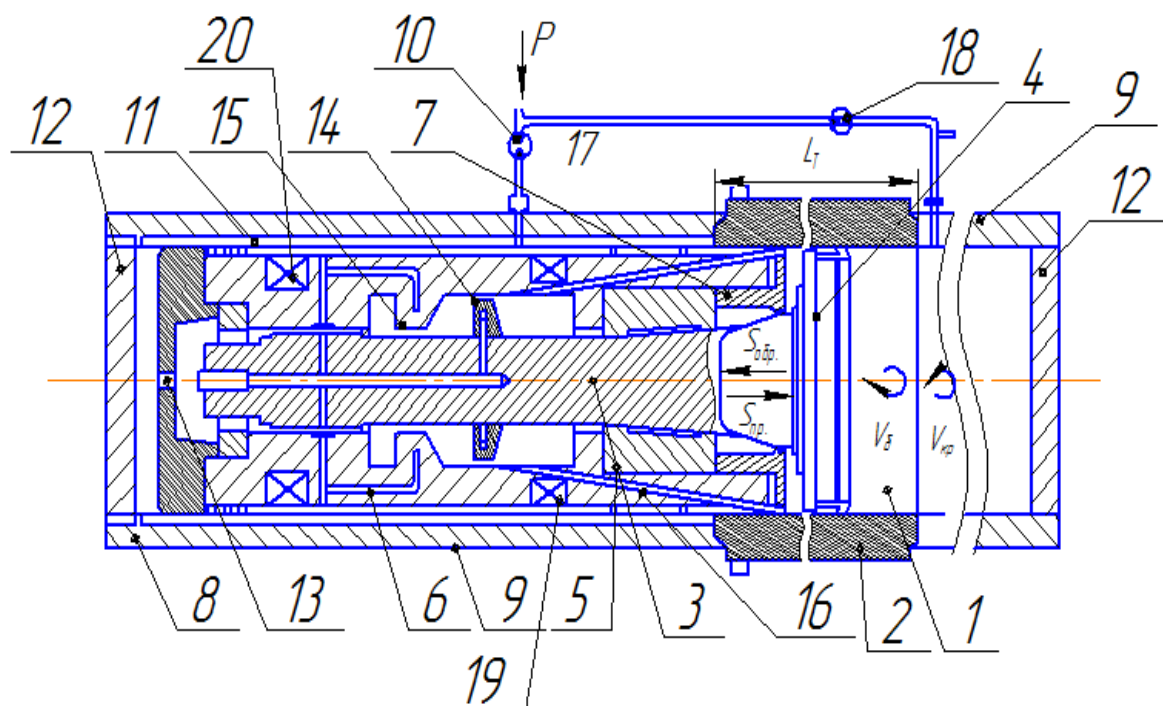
Малогабаритный станок с режуще-деформирующей пинолью для вихрефрезерования или внутреннего шлифования ГО труб методом винтовой интерполяции
